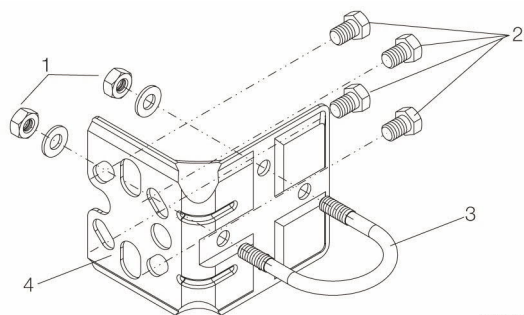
Flachhalterung zur Rohrmontage - Barrel-Gehäuse
